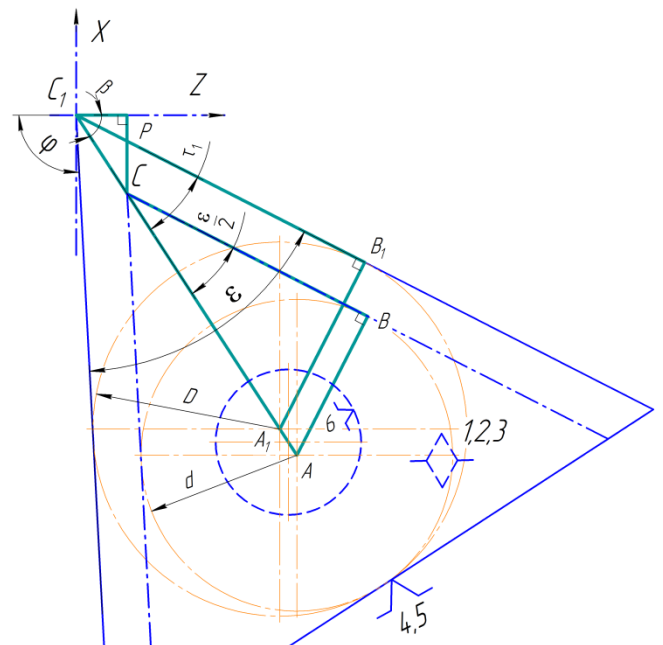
Схема для расчета погрешности базирования пластины по допуску на диаметр вписанной окружности СНП при креплении клин-прихватом
